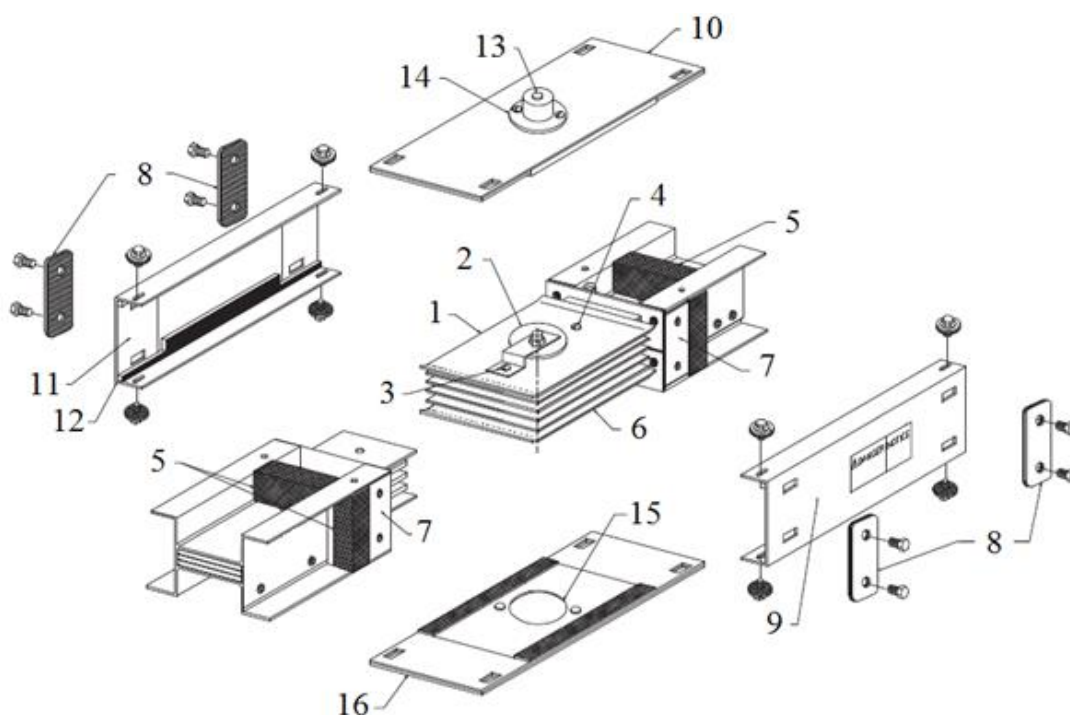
Схема соединения секций шинопровода наружной установки: 1 – верхняя пресс-пластина стыковочного блока; 2 – шайба; 3 – болт крепления фиксирующей пластины; 4 – фиксирующий болт; 5 – герметизирующая прокладка; 6 – нижняя пресс-пластина стыковочного блока; 7 – контактная пластина корпуса секции; 8 – шайба-пластина; 9 – боковая крышка; 10 – верхняя крышка; 11 – контактная пластина боковой крышки; 12 – герметизирующая прокладка боковой крышки; 13 – отверстие заглушки; 14 – заглушка болта стыковочного блока; 15 – отверстие для доступа к болту стыковочного блока; 16 – нижняя крышка стыковочного блока.
